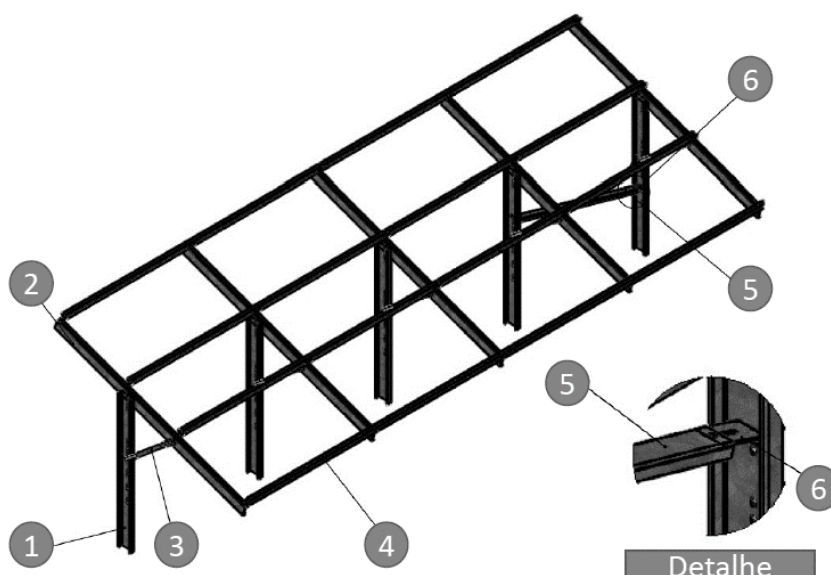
Elementos que compõem a estrutura das placas - Geral
